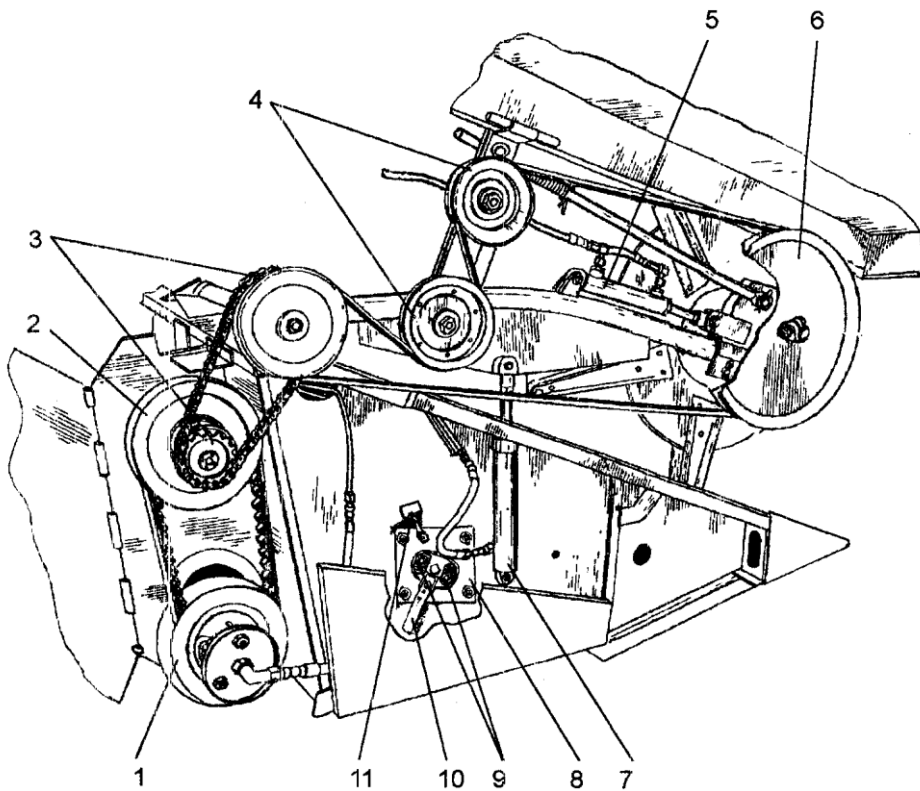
Жатка (правая сторона): 1 – нижний шкив вариатора; 2 – верхний шкив вариатора; 3 – звездочка; 4 – шкивы натяжные; 5 – гидроцилиндр выноса мотовила; 6 – шкив большой; 7 – гидроцилиндр подъема мотовила; 8 – плита; 9 – гайки; 10 – рукоятка регулировки пальчикового механизма; 11 – гайка регулировки установки шнека по высоте
